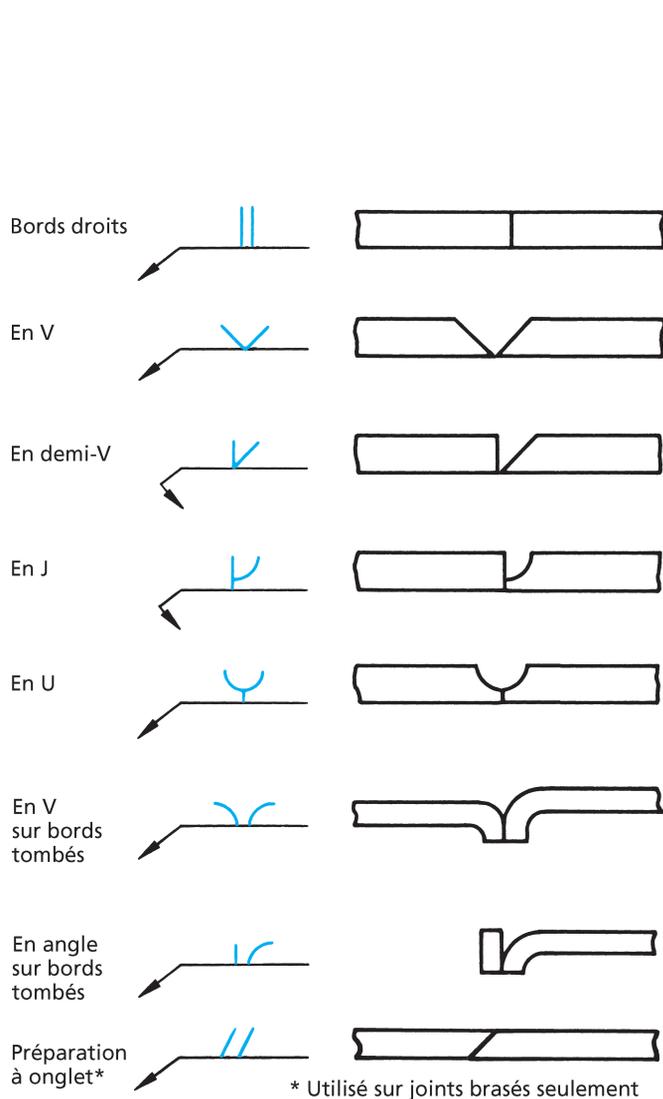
■ Symboles de soudure et assemblages avec chanfrein.
